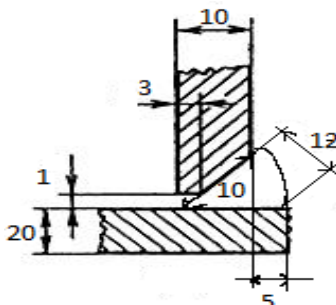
Геометрические размеры сварного шва, мм
